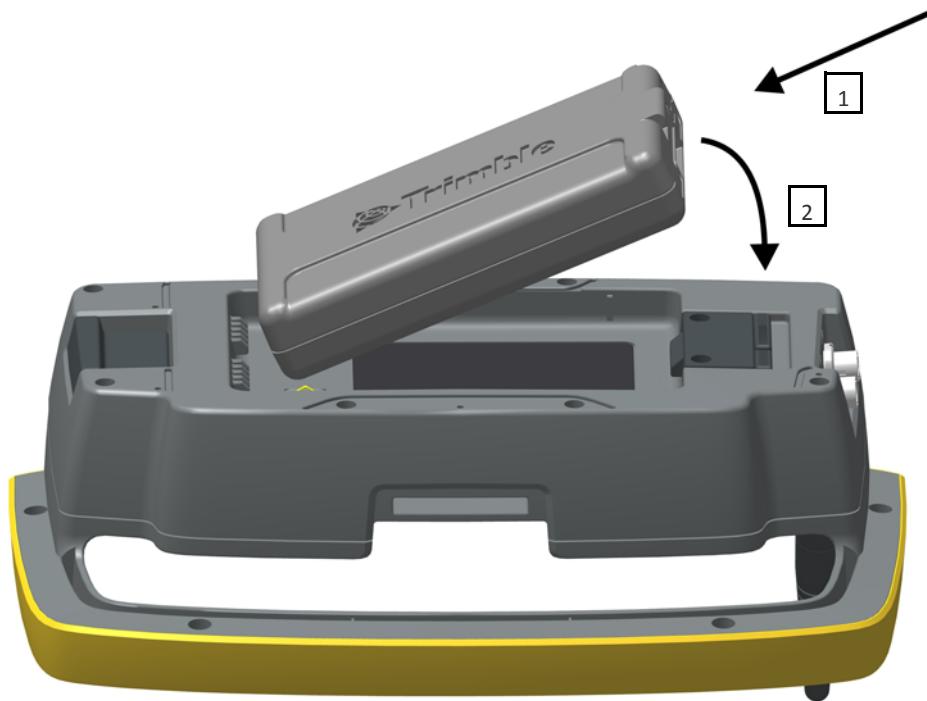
Установка батареи в держатель Trimble Robotic
